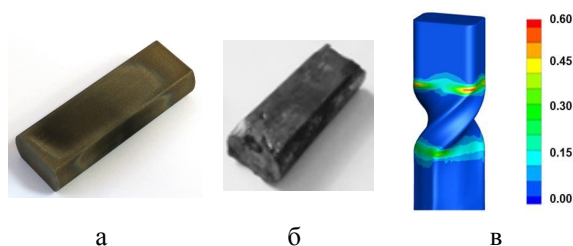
Общий вид исходной призматической заготовки для ВЭ (а), заготовки после ВЭ (б) и поле интенсивности скорости деформации заготовки в процессе ВЭ, c^{-1} (в)
